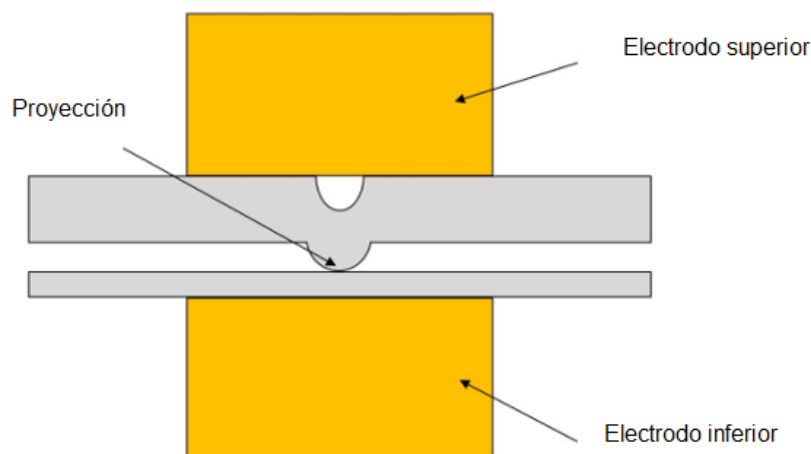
Soldadura por proyección para tornillos y tuercas. [F-44]
